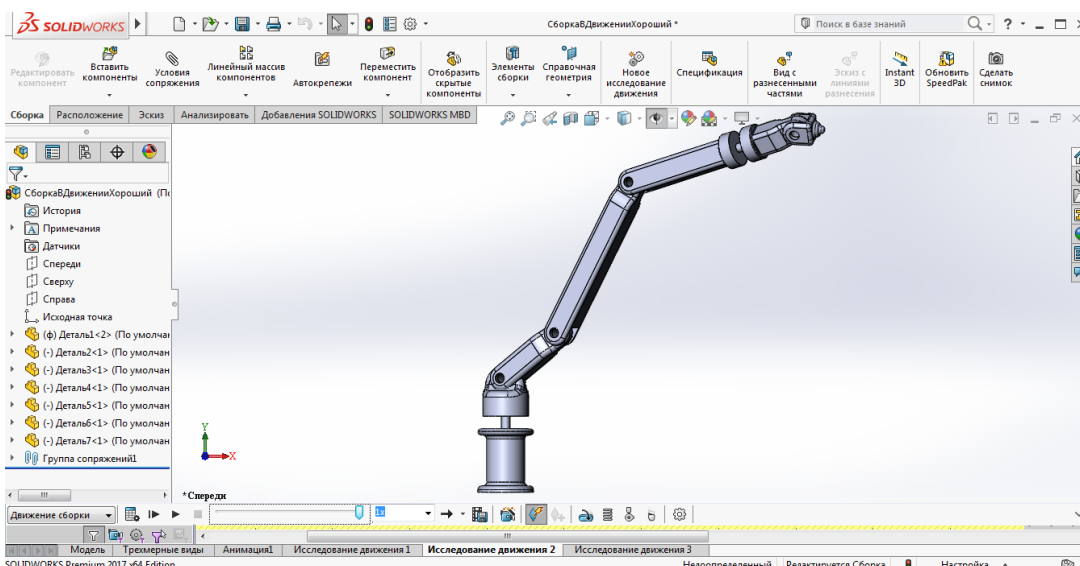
Робот завершил прохождение сварного шва
